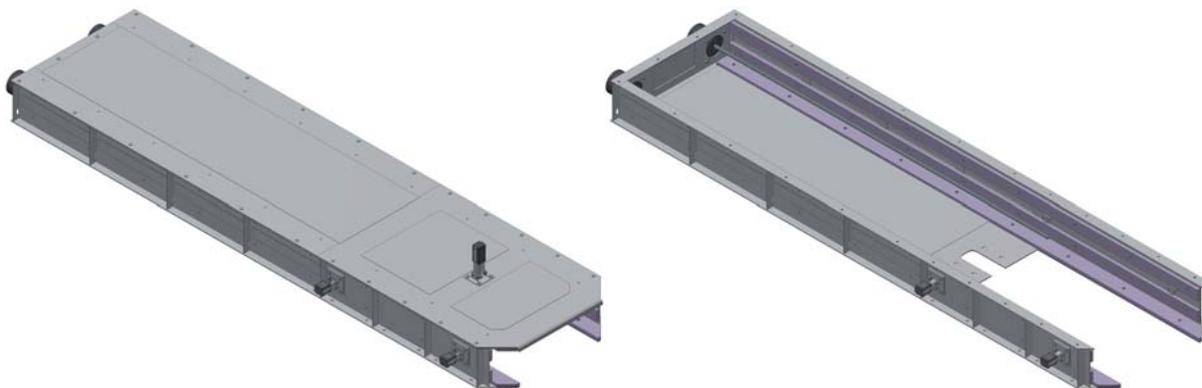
Hauptbaugruppe Tunnel mit (li.) und ohne (r.) Tunneldeckel
